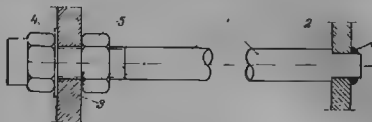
Деталь установки стяжного болта в водяной камере конденсатора
